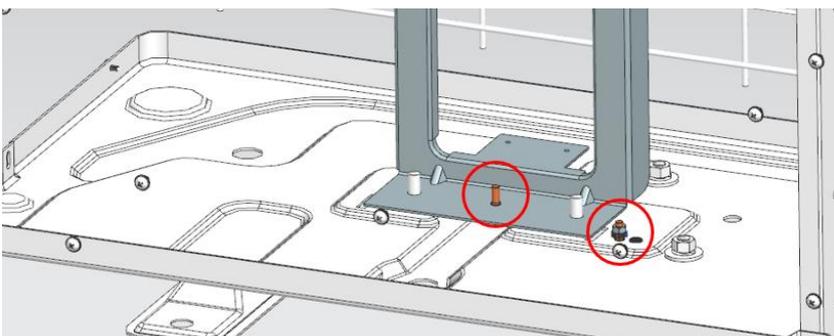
Raccordement à la terre sur le support de ventilation et la plateforme
